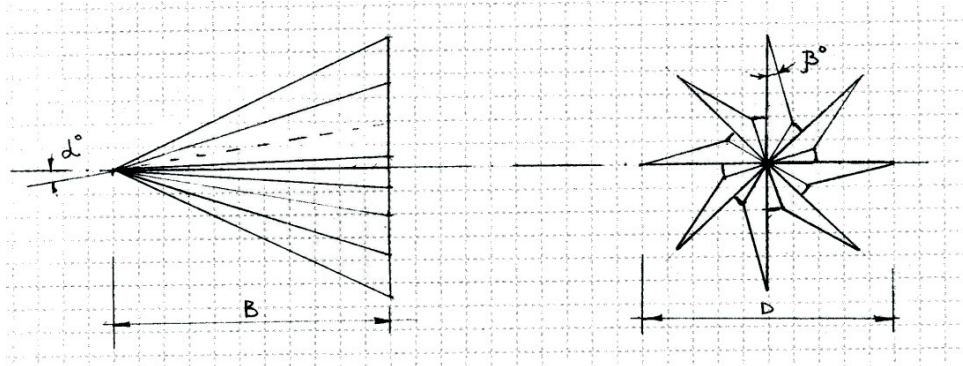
Схема конструкции создающей турбулентный поток для очистки трубопровода от илистых отложений
